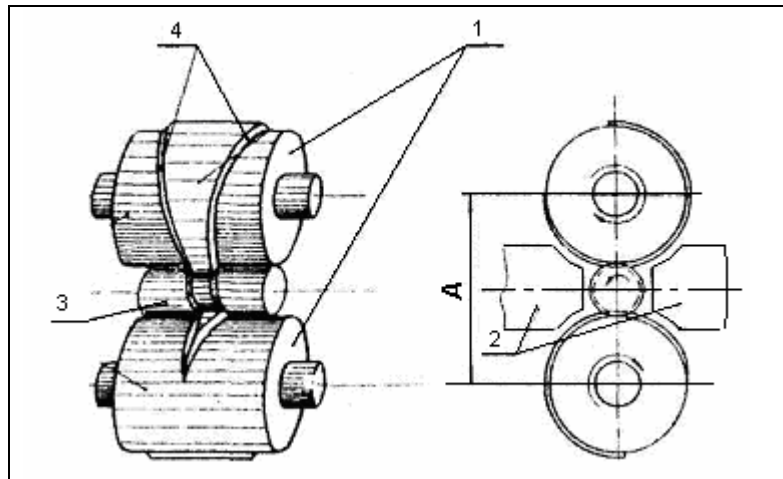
Схема поперечно-клиновой прокатки: 1- валки; 2 - направляющая линейка; 3 -заготовка; 4 - клиновидный калибр;
